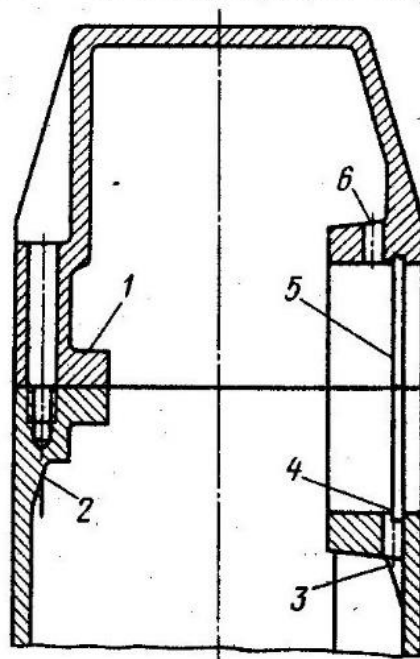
Сечение корпуса по оси вала и по стяжному винту, соединяющему крышку с корпусом:
